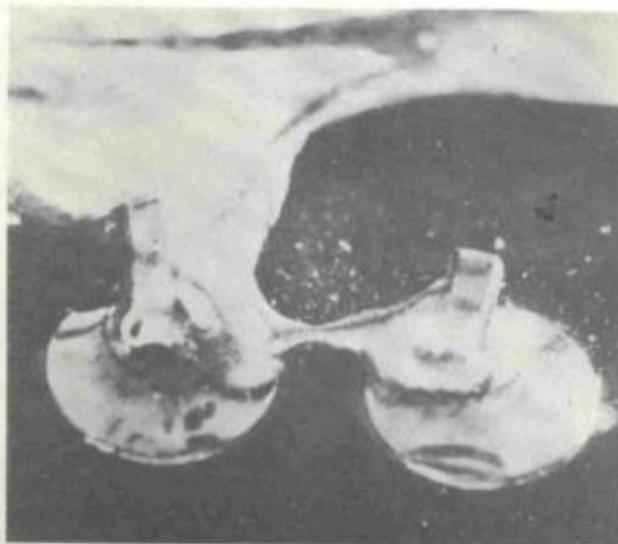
Ponte de solda entre terminais de componente devido a espaçamento incorreto ou condições incorretas de soldagem.
